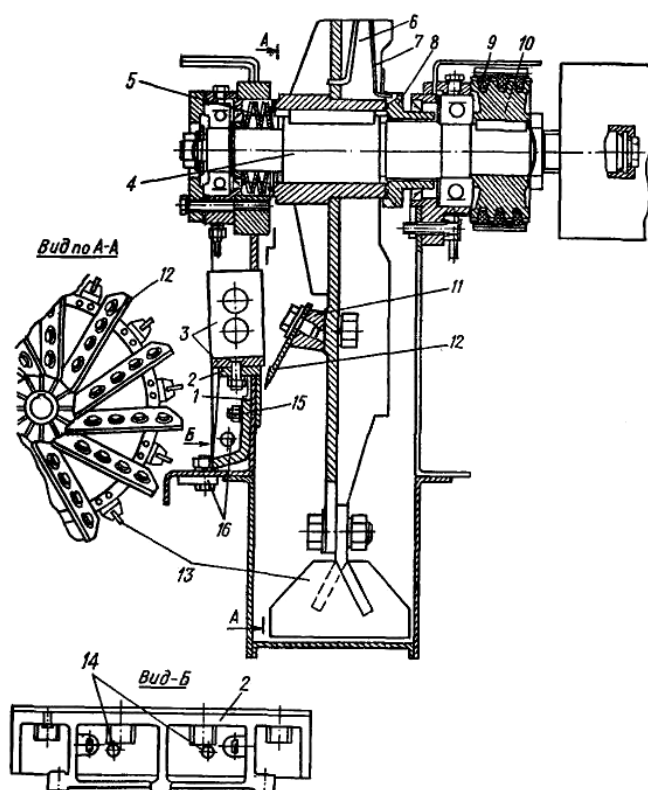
Аппарат измельчающий КПК-3000: 1 – камера, 2 – подбрусник, 3 – противорежущая пластина, 4 – вал, 5 – тарельчатая пружина, 6 – ротор измельчителя, 7 – стопорная пружина, 8 – гайка, 9 – ремень клиновой, 10 – шкив, 11 – опора ножа, 12 – нож, 13 – лопатки, 14 – регулировочный болт, 15, 16 – болты крепления подбрусника
